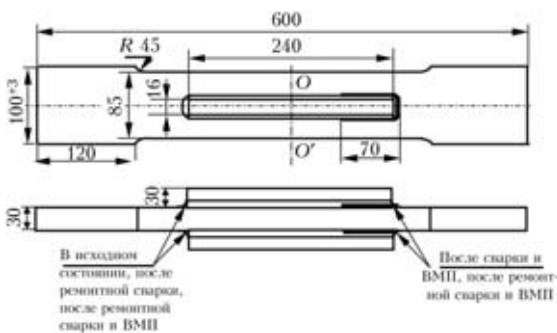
Размеры образца для оценки эффективности применения ВМП изготовленных и отремонтированных сварных соединений
